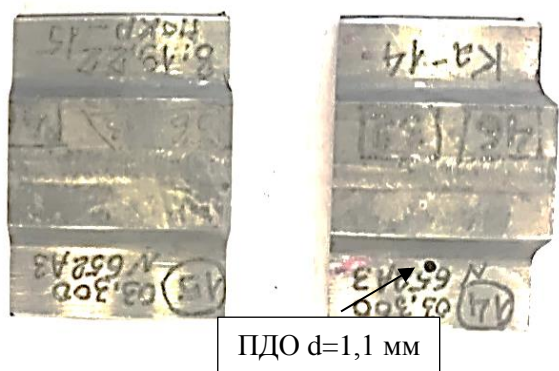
Фотография бездефектного образца №1 и образца №2 с искусственным дефектом
